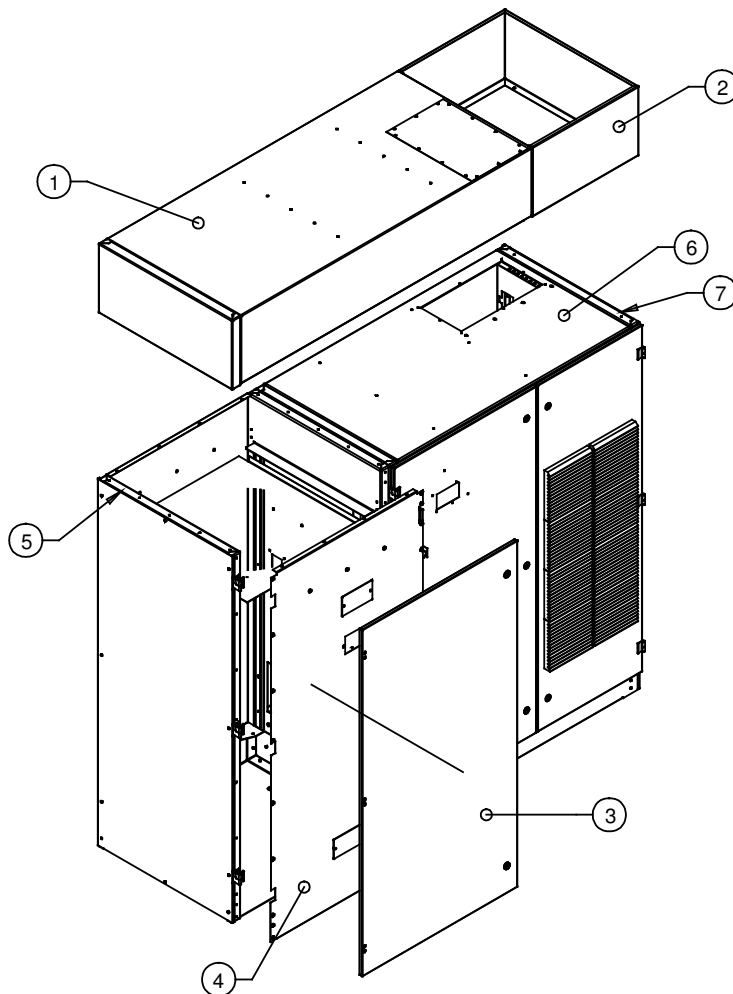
Einzelteile UB220 – UB330 Schalldämpfer
